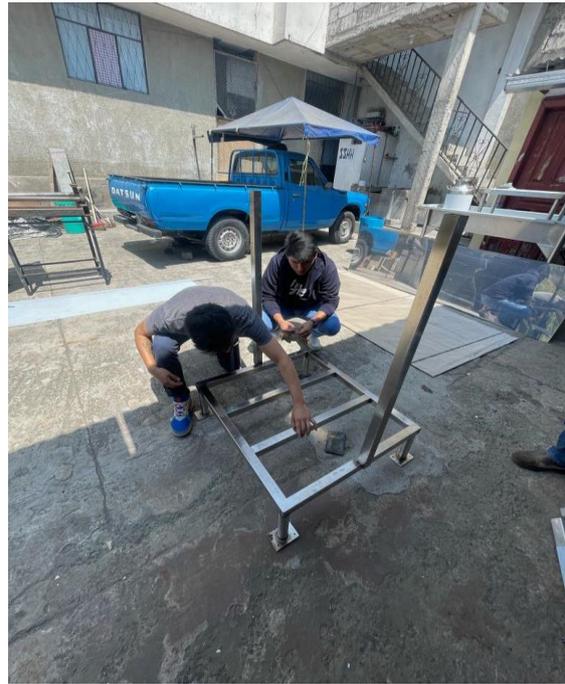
Proceso de soldadura y armado, bases de prensa mecánica.
